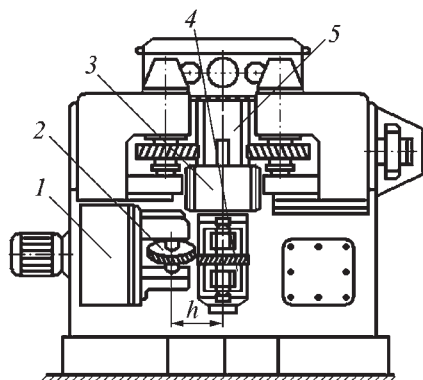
Станок для холодного калибрования зубьев цилиндрических колес с устройством стабилизации припуска под калибрование
